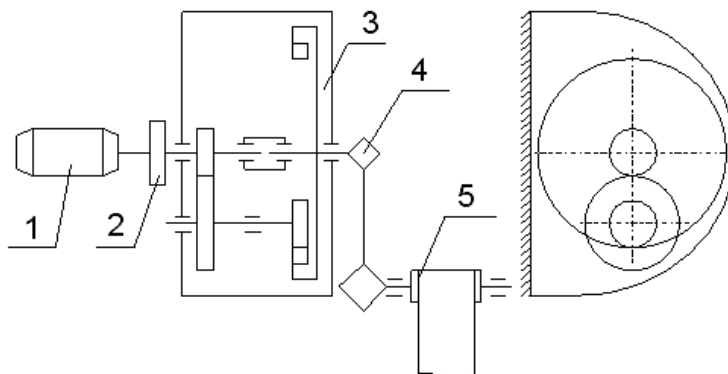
Привод ленточного конвейера: 1 – электродвигатель; 2 – муфта; 3 – редуктор; 4 – цепная передача; 5 – барабан
